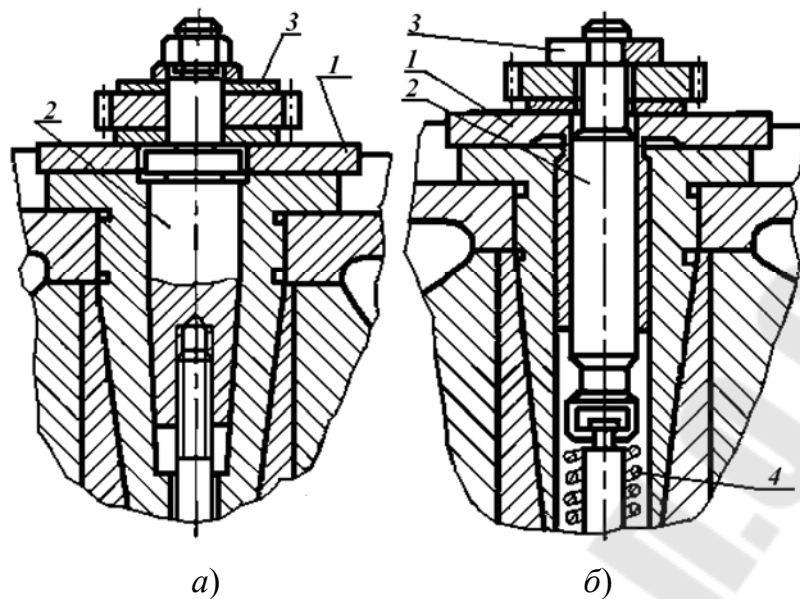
Эскизы установки и закрепления заготовки:
